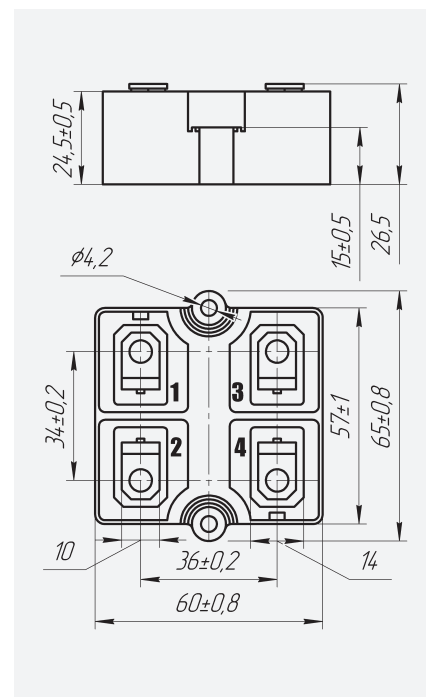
Габаритный чертеж резистора P1-150M (исполнения 1 и 3) и наборов резисторов NP1-82 (исполнения 2, 3, 4 и 5)
